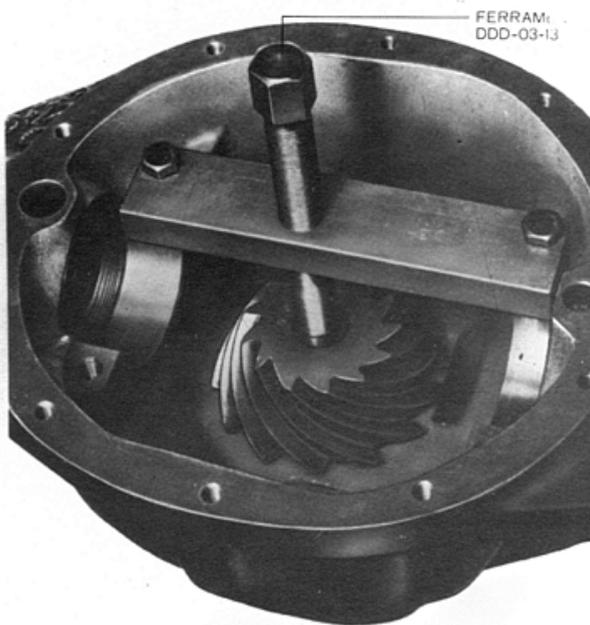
Instalação do pinhão e da ferramenta de fixação do pinhão
